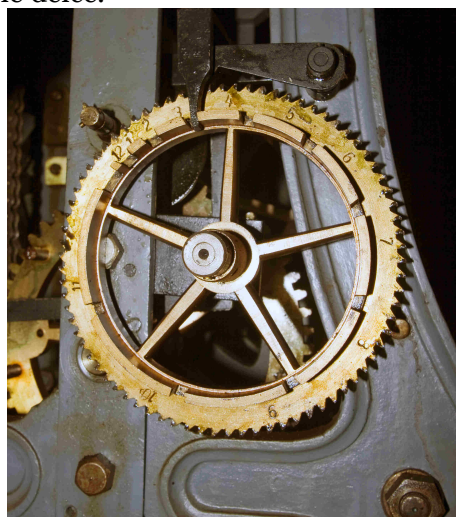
Krokový mechanismus a detail zavěšení kyvadla.
